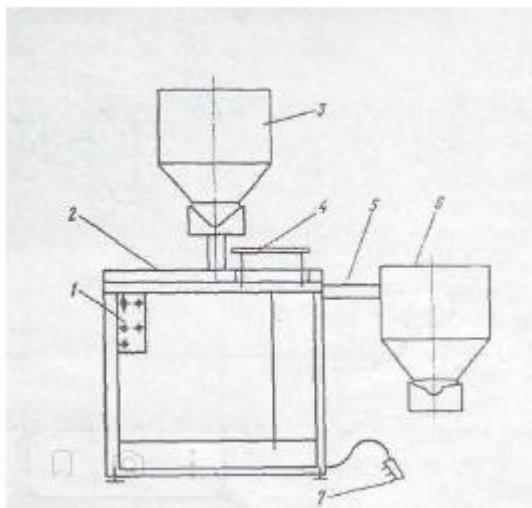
Установка УФ-158 для фасования продовольственных товаров: 1 – панель управления; 2 – стол; 3, 6 – бункеры; 4 – сварочное устройство; 5 – г-образная вилка; 7 – педаль
